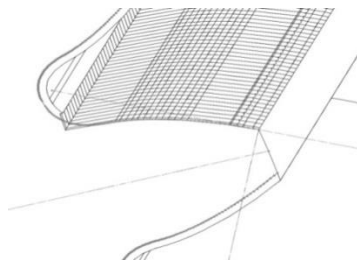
Схема формообразования сетки на обрабатываемой поверхности зубчатого колеса
